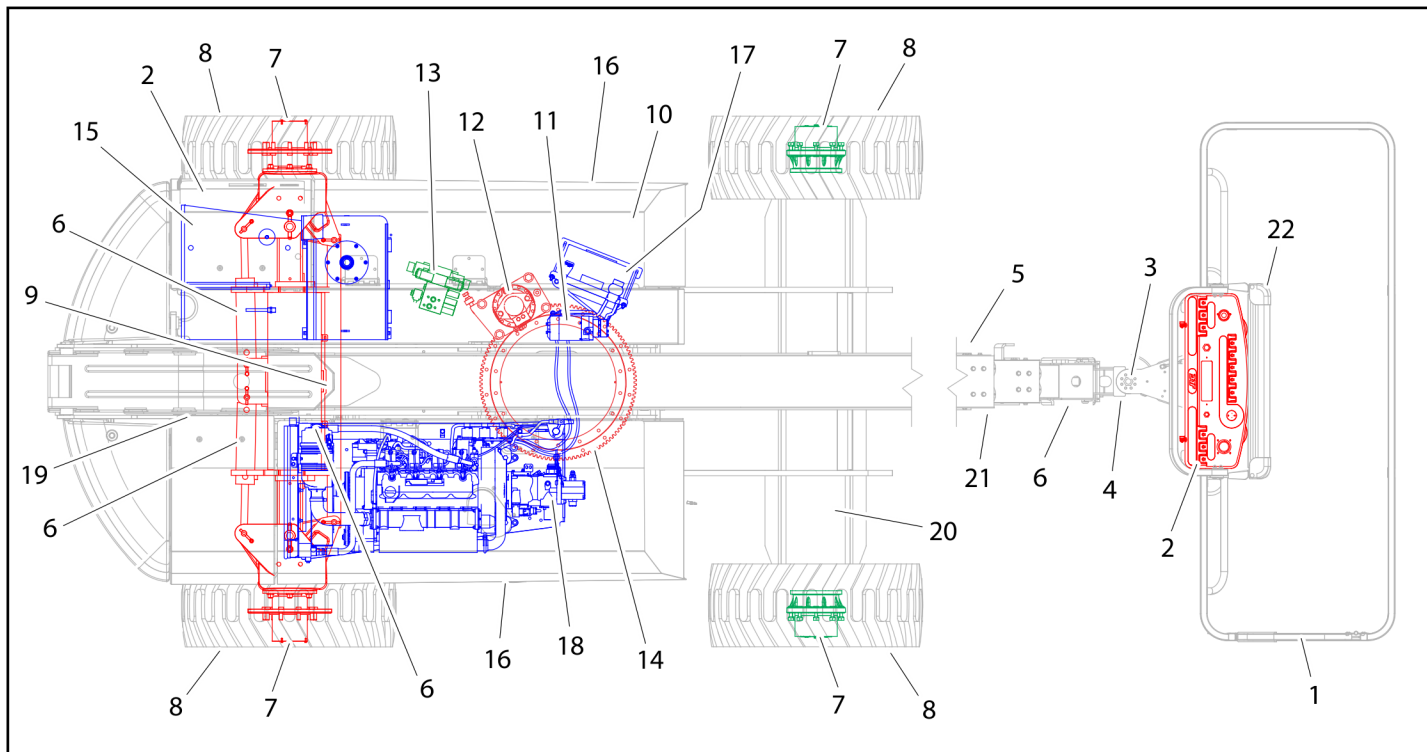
Schemă pentru inspecția vizuală zilnică
